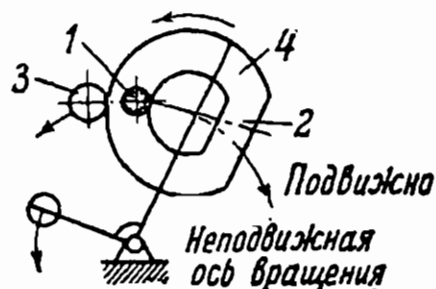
Схемы фрезерования по копиру. 1—фреза, 2—деталь, 3—ролик, 4—шаблон.
